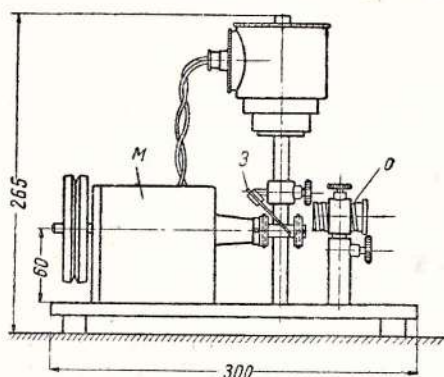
Прибор для проверки профиля зубьев барабанов и качания зубьев скачковых барабанов
